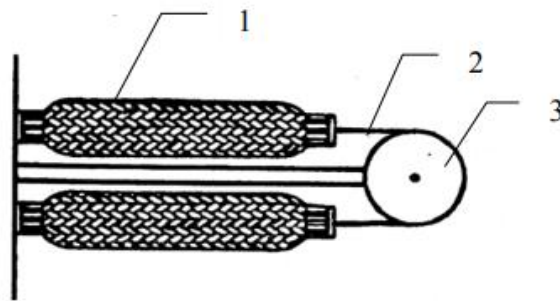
Реверсивний гнучкий пневматичний привід компанії «Бріджстоун», де: 1 – гнучкий пневматичний привід; 2 – трос; 3 – блок.
